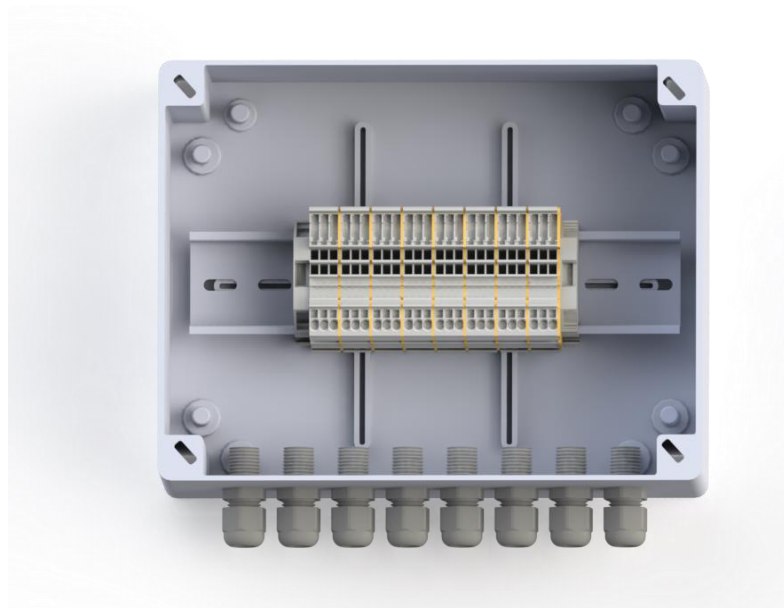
Общий вид ящика подключения ручного считывателя ЯП-01-XX
